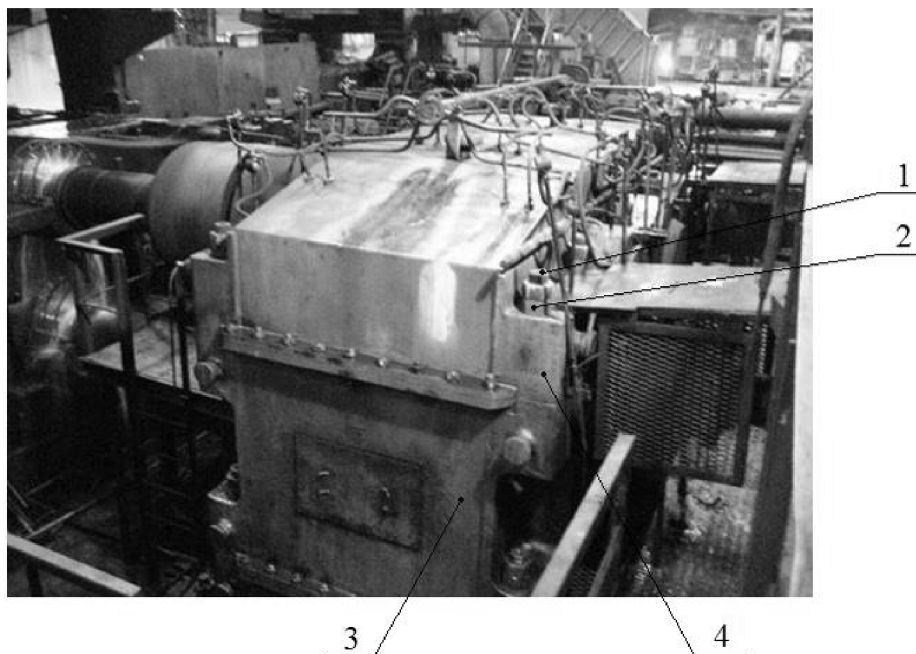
Редуктор главного привода клетки №1 стана 2000:
